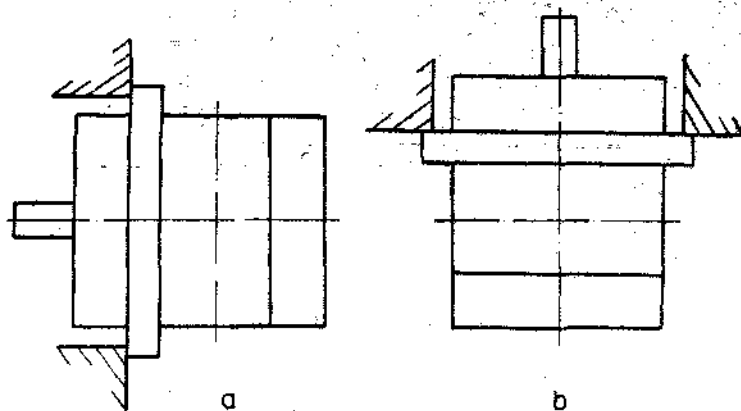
Mașini fără tălpi, cu scuturi portlagăr și flanșă pe carcasă:
